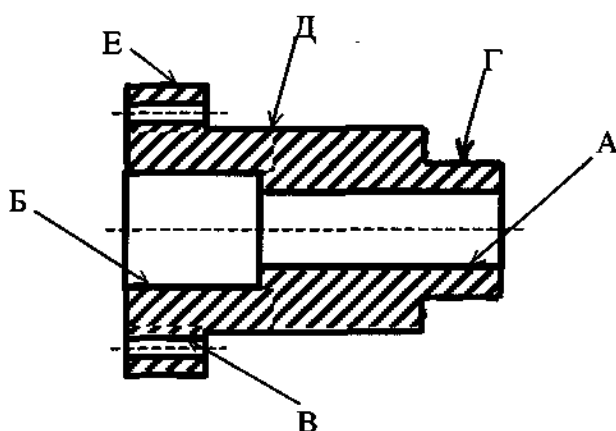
Эскиз детали с указанием заданных обозначений размеров и шероховатости поверхностей
